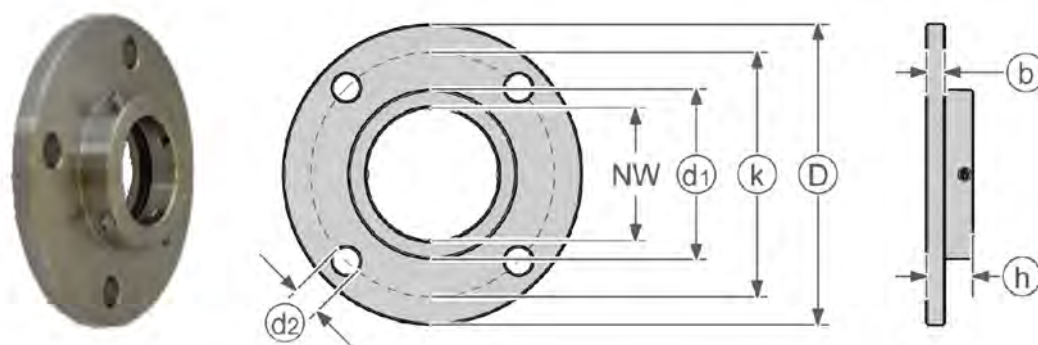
Dimensões do flange deslizante do queimador de ignição GFI
